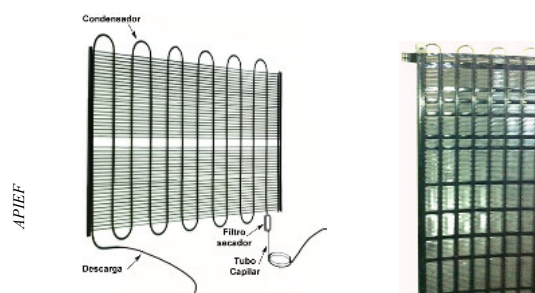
Sistemas com condensador em tubo com varetas soldadas
